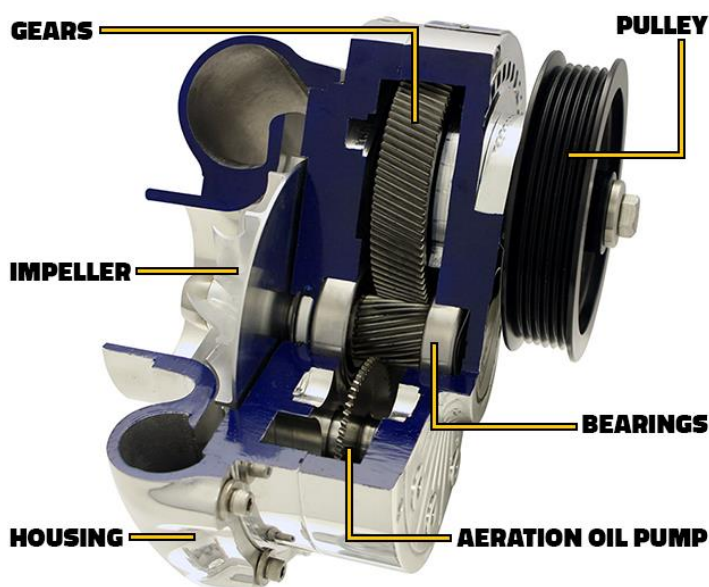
Центробежный нагнетатель в разрезе [29]
